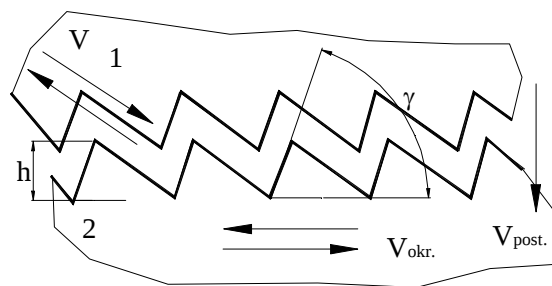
Развертка зубчатого зацепления по внешнему диаметру
